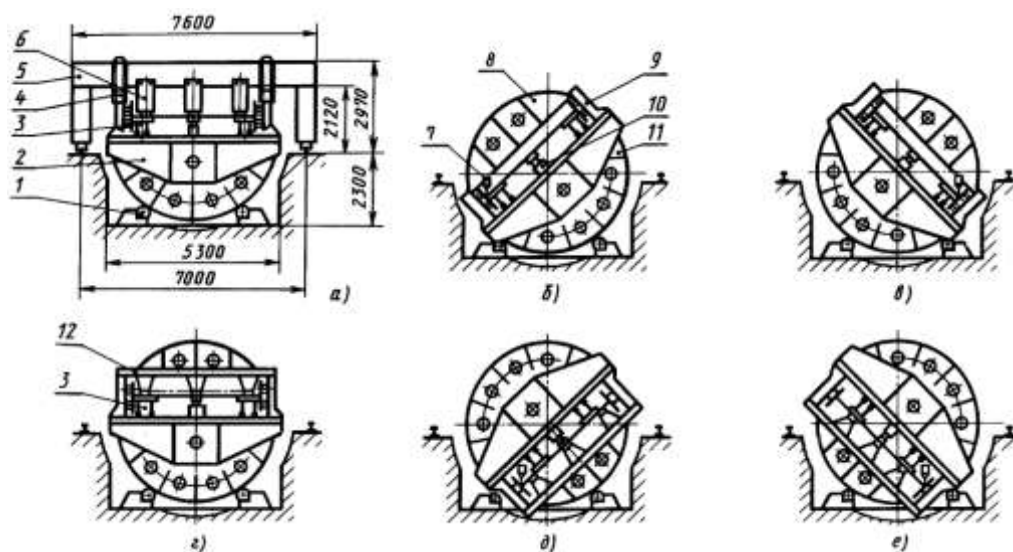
Основные этапы сборки и сварки двутавровых балок в полноповоротных кондукторах
